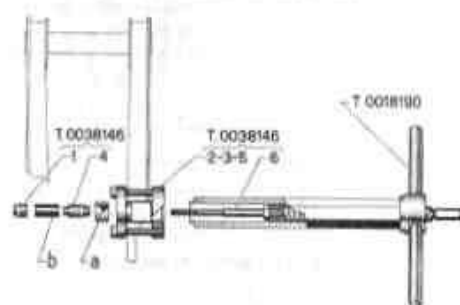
Rimontaggio tampone elastico e tubo interno
